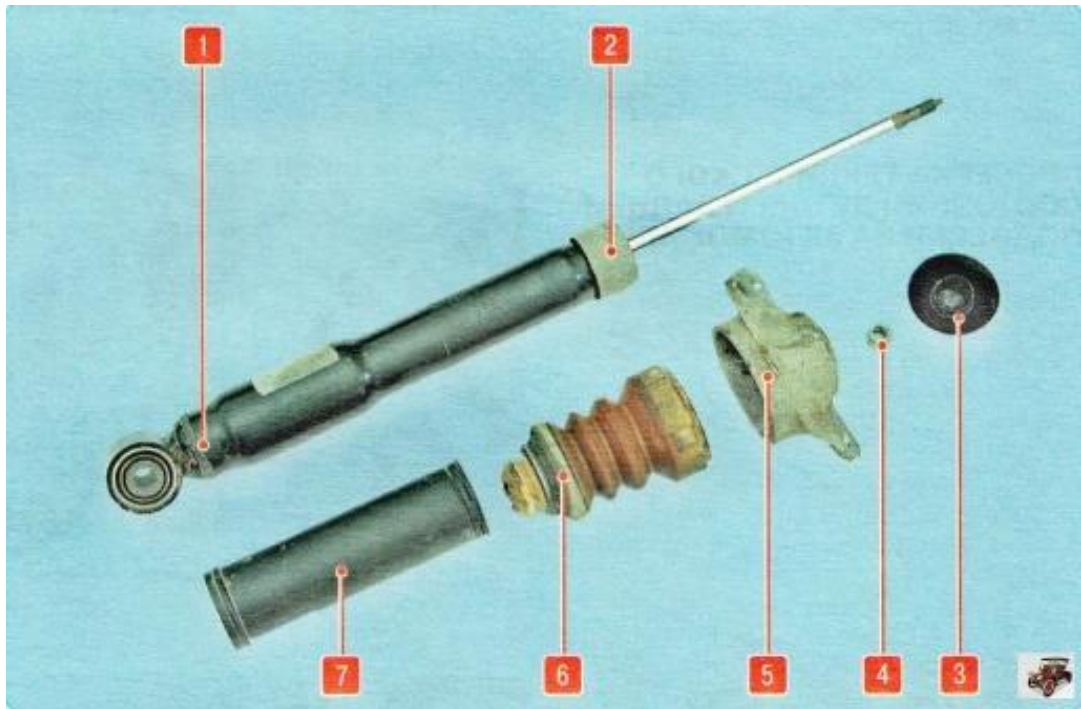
Амортизатор задньої підвіски: 1 – робочий циліндр амортизатора; 2 – кришка; 3 – кришка гайки штока; 4 – гайка штока амортизатора; 5 – опора амортизатора; 6 – відбійник; 7 – пильник.
